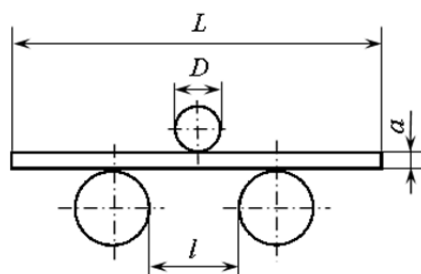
Схема испытаний на изгиб с использованием двух опор и оправки
